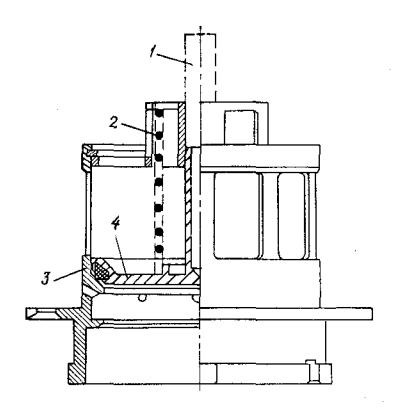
Бортовой штуцер заправки I - шток; 2 - пружина; 3 - корпус; 4 - клапан
